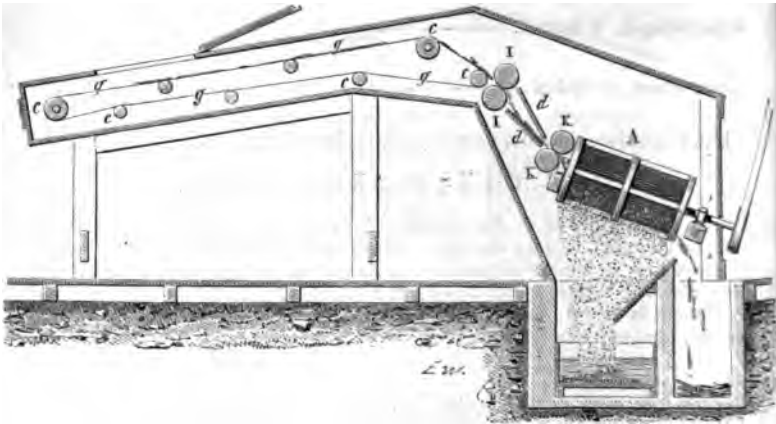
Machine à découper le plomb recouvert de céruse.
